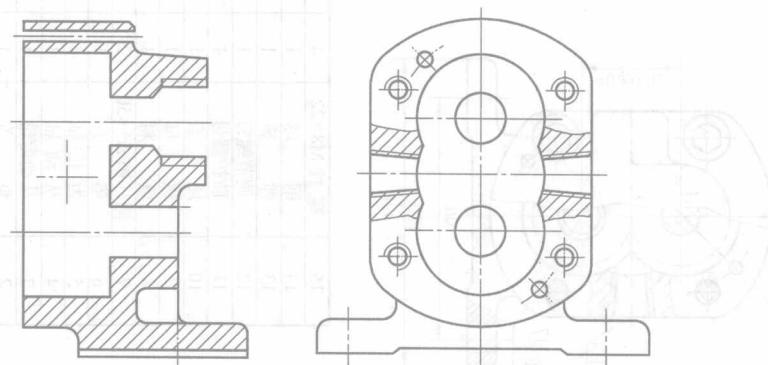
6 从装配图中分离出来的泵体主视图、左视图轮廓
